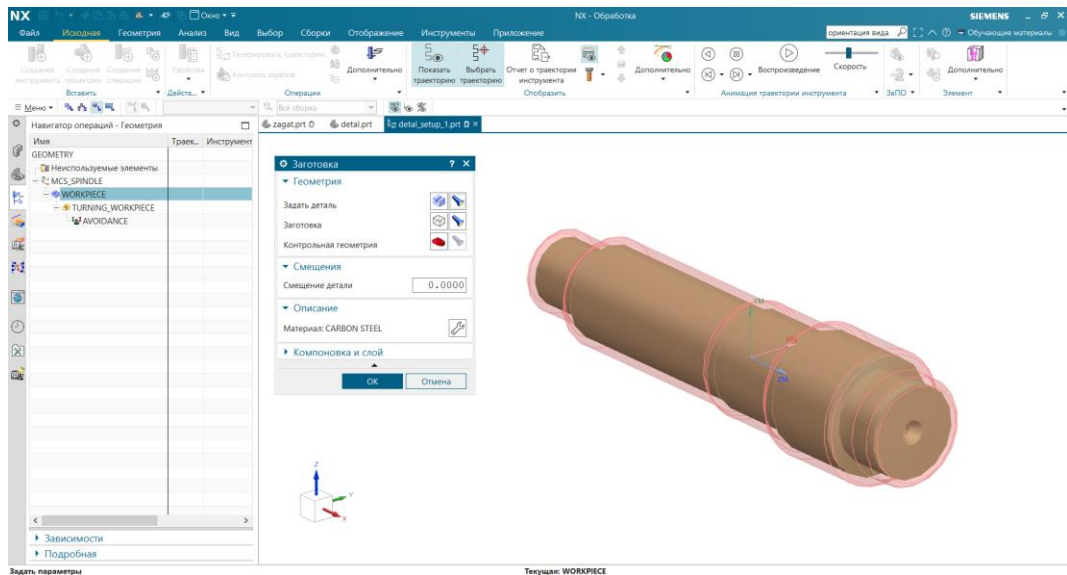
Визначення деталі, заготовки в системі NX CAM
